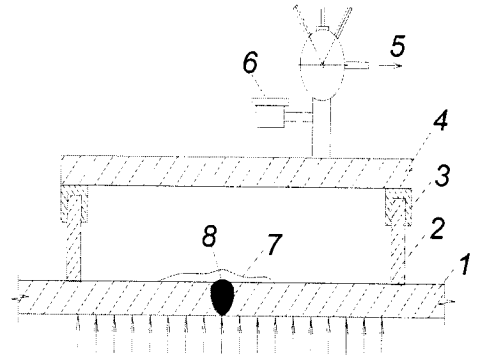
Схема установки для вакуумно-бульбашкового контролю:
